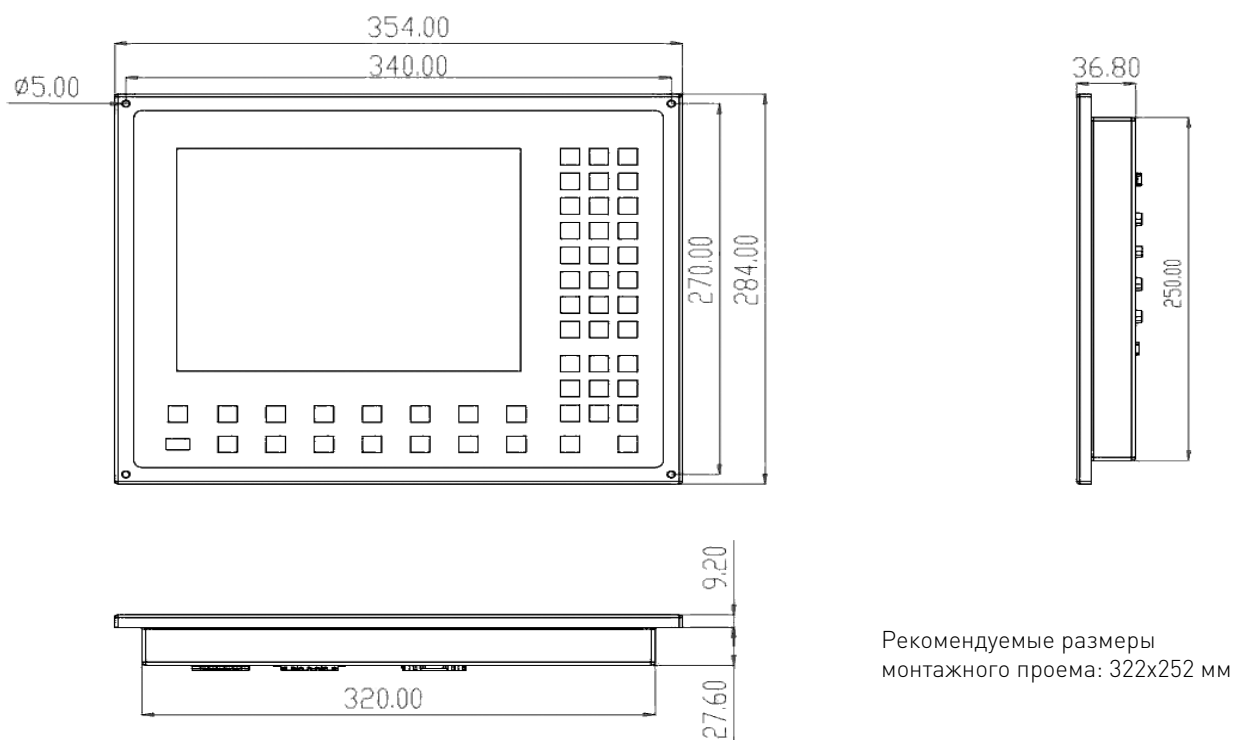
Установочные размеры ЧПУ контроллера FX430A.
